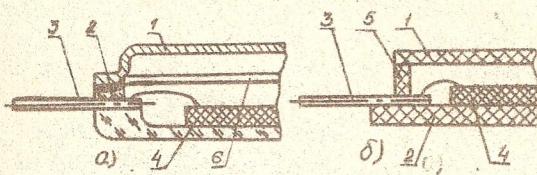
Стеклянный (а) и керамический (б) корпус типа 4:
